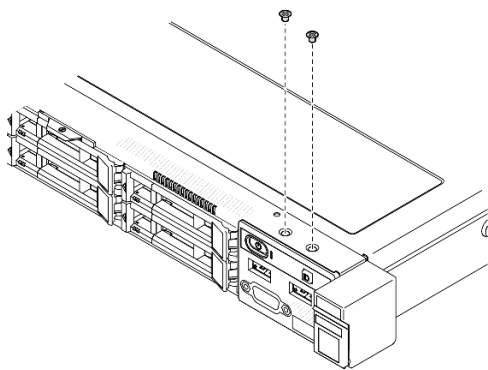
Remoção dos parafusos do módulo de E/S frontal
